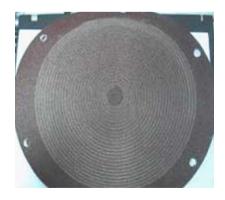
测试后砂纸表面的螺旋线 FIG. 2 spiral line on the coated abrasive disk after test
